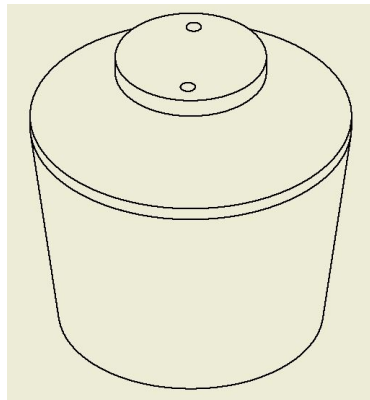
Quinto prototipo de la boya, parte de arriba (vista alzada)
